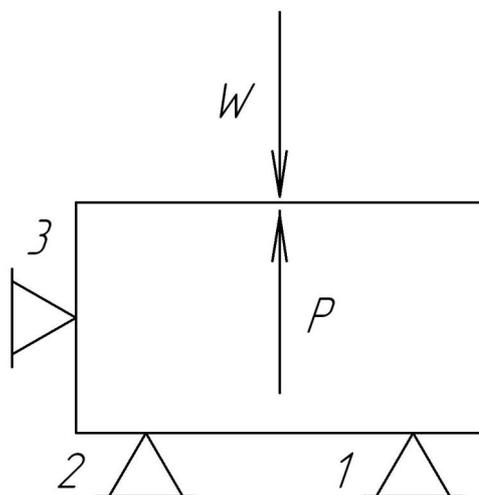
Схема установки, при которой силы резания стремятся оторвать заготовку от опор
